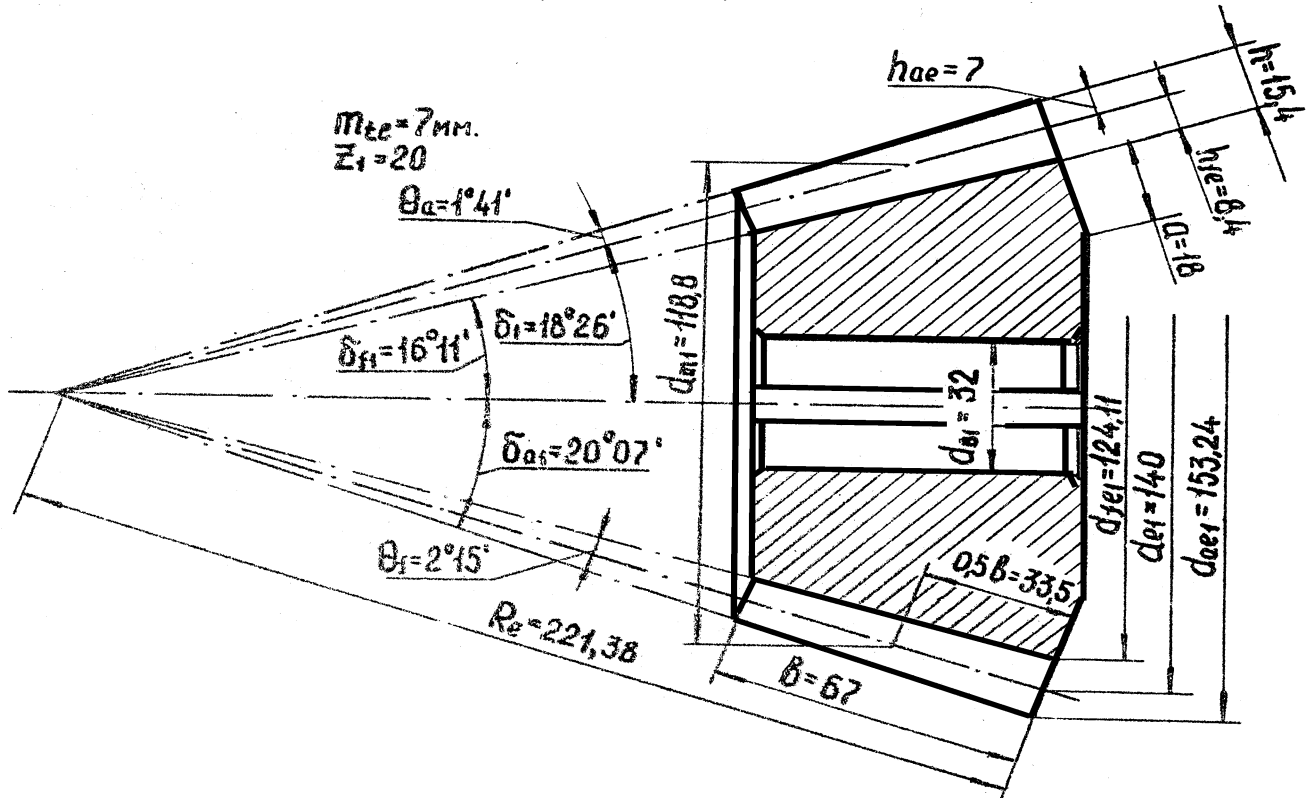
Ескіз конічної прямозубої шестерні
